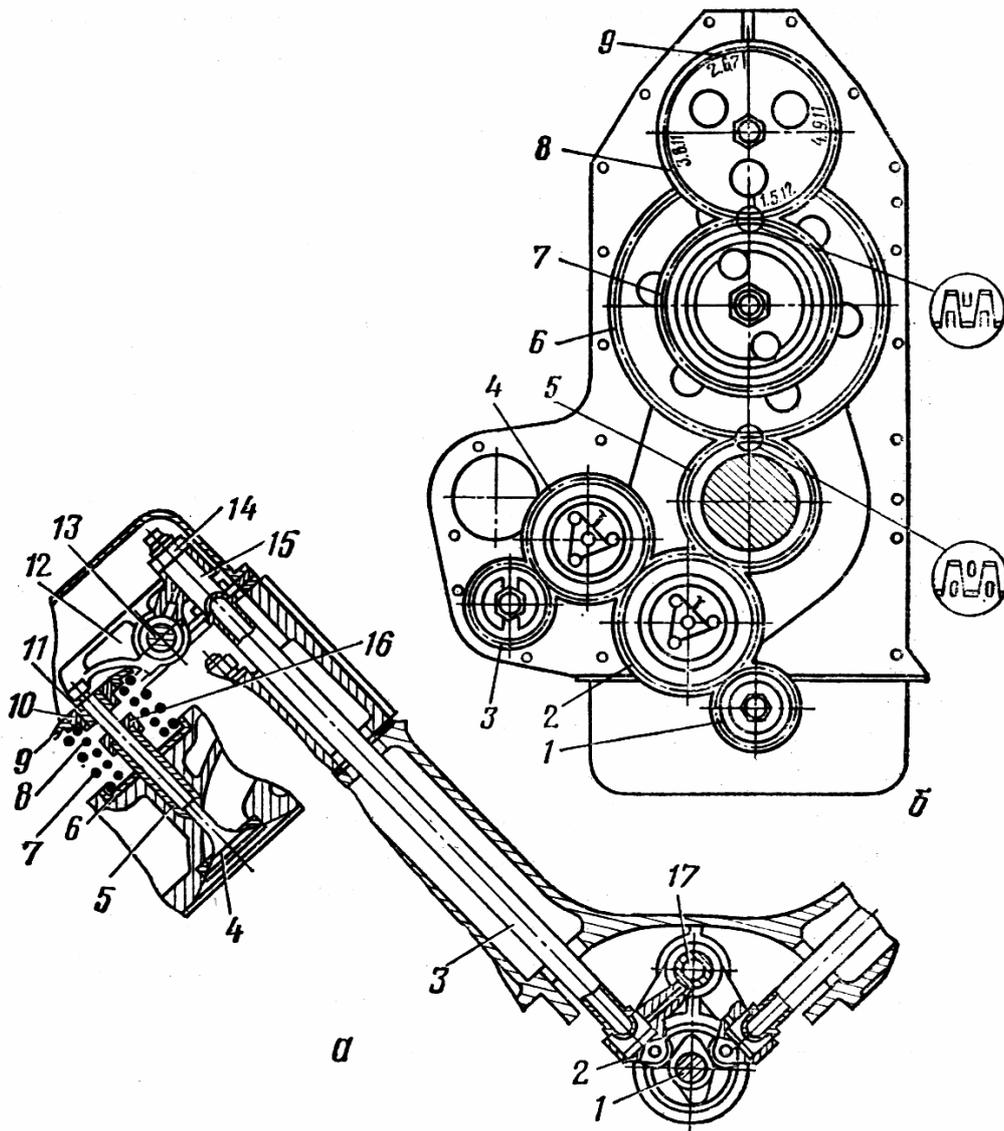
Газораспределительный механизм двигателя ЯМЗ-240Б:
